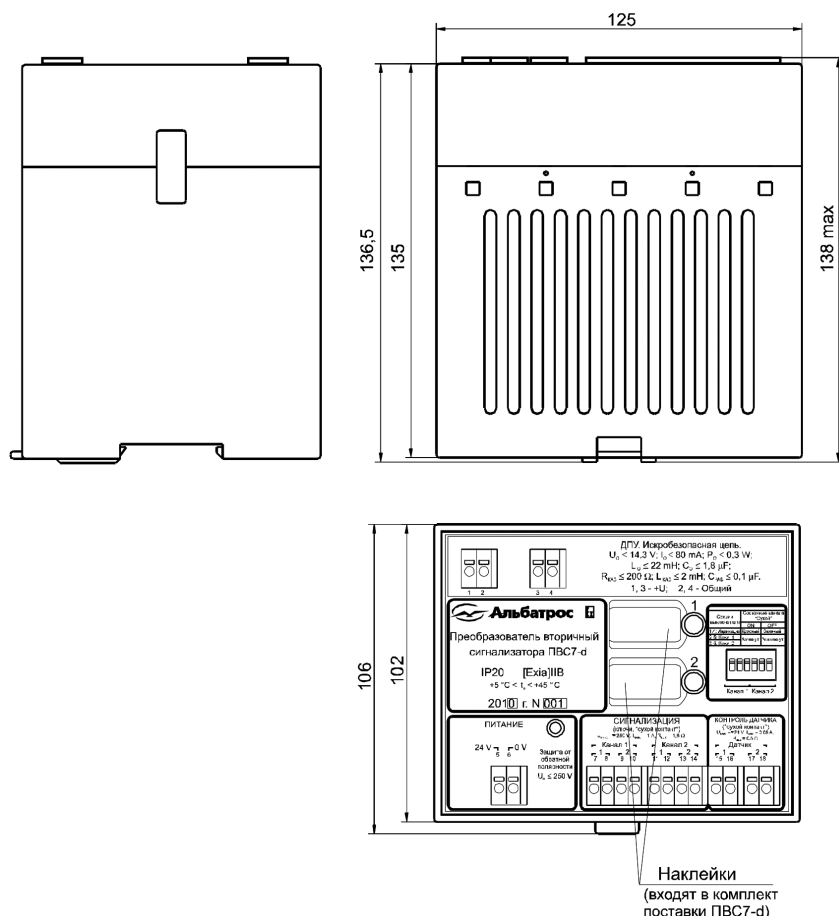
Габаритные размеры вторичного преобразователя ПВС7-d
